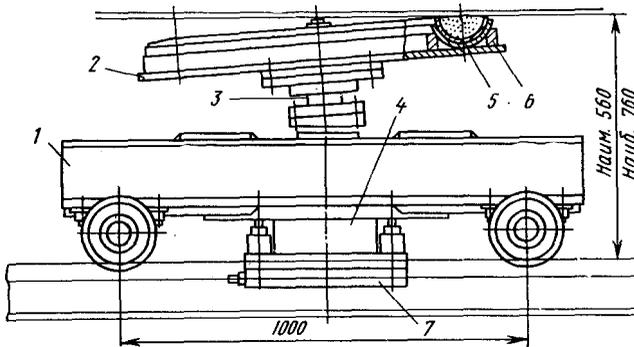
Флюсовая подушка с эластичным лотком для сварки кольцевых швов
